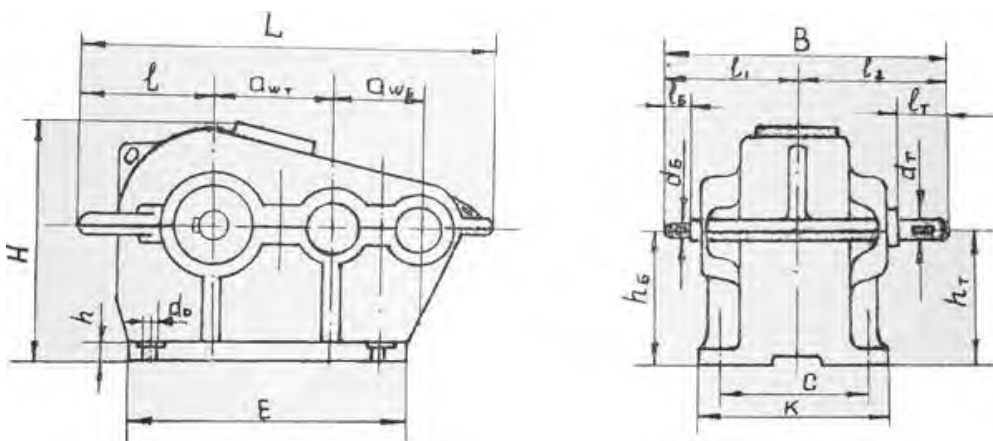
Габаритные и присоединительные размеры цилиндрического редуктора
